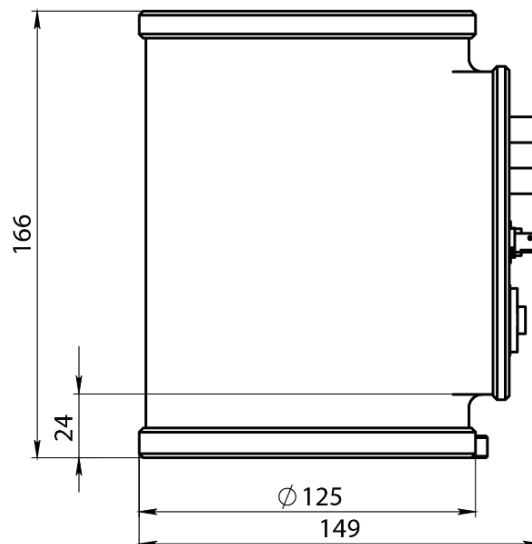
Robyhead D1 габаритные размеры нижней части.
